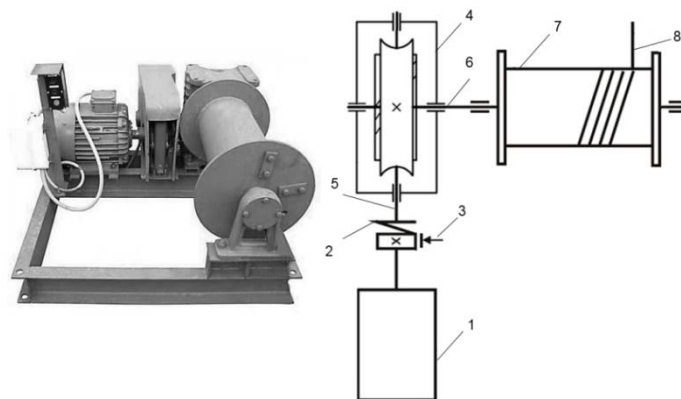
Внешний вид (слева) и кинематическая схема (справа) реверсивной электрической лебедки с червячным редуктором: 1-электродвигатель; 2-муфта; 3-тормоз; 4-редуктор; 5-быстроходный вал редуктора; 6-тихоходный вал редуктора, 7-барабан, 8-канат
